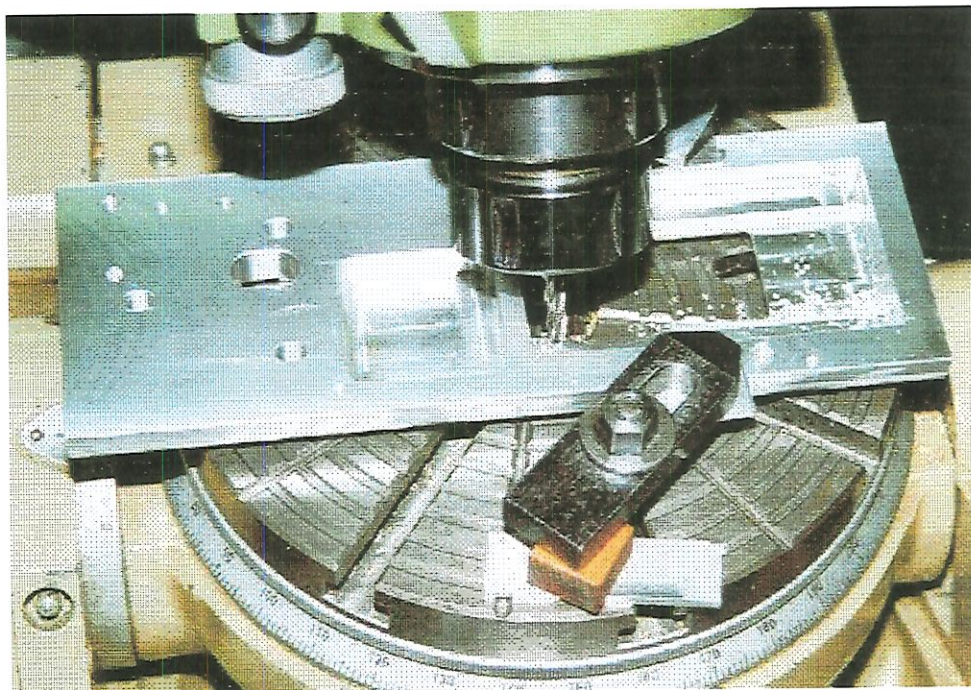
Usinagem da chapa inserida na base do microscópio.
